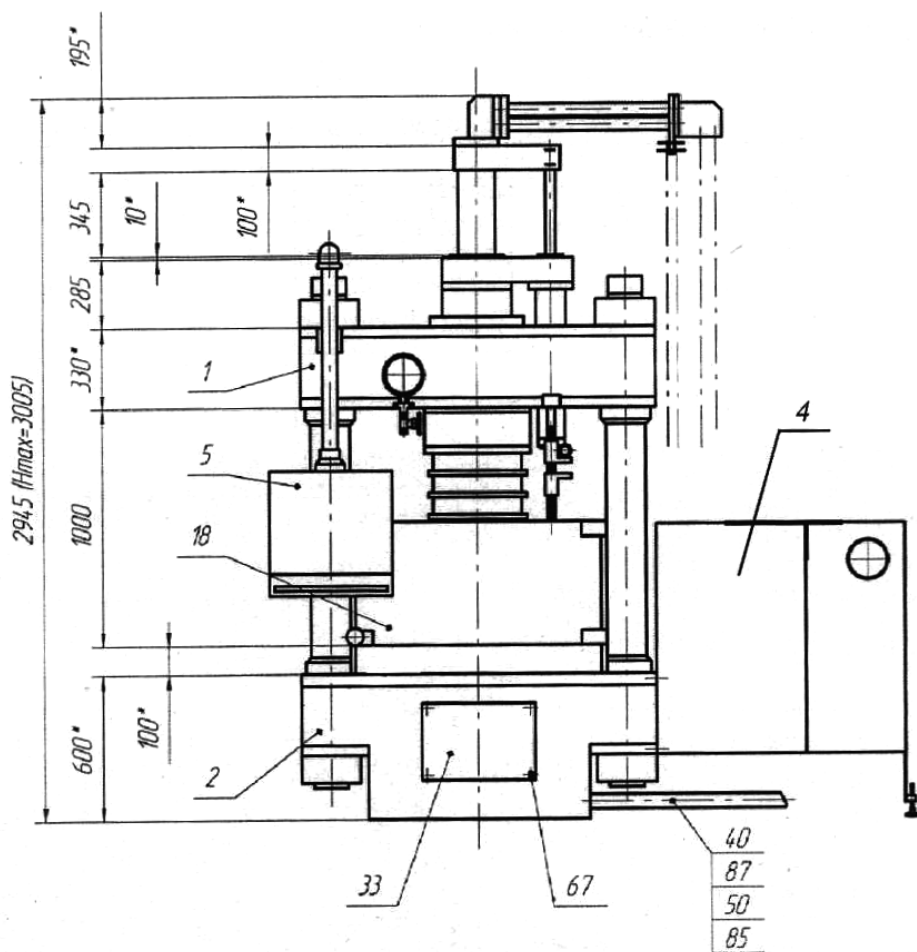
Верстат «АМ-1» (вид спереду)
